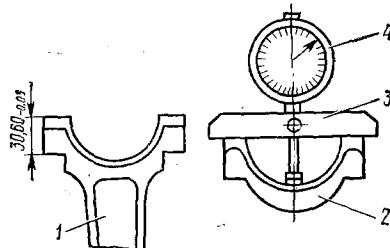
Схема измерения глубины фрезерования плоскости разъема крышки и шатуна:
